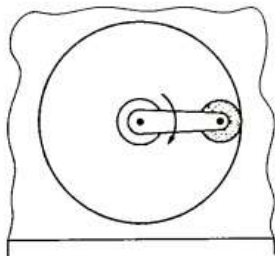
Планетарне шліфування отворів корпусних деталей
